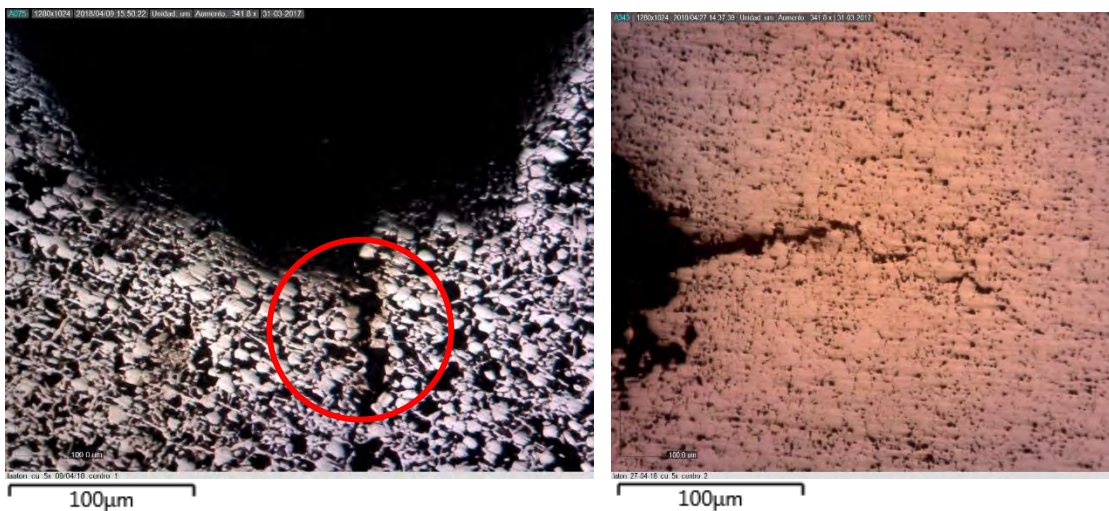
Agrietamiento inducido por fuerzas de torque a la pieza de latón en molde de acero a 5x por MO, a) Inicio de propagación de la grieta y b) final del agrietamiento (tomada de lado horizontal).
